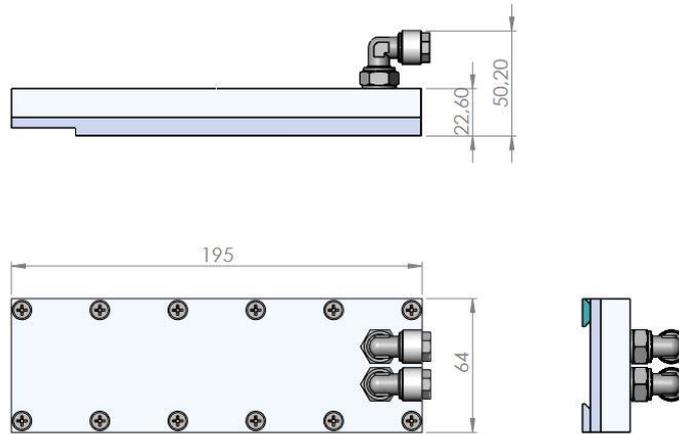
Wasserkühlmodul – Technische Ansicht (Quelle: Autovimation)
